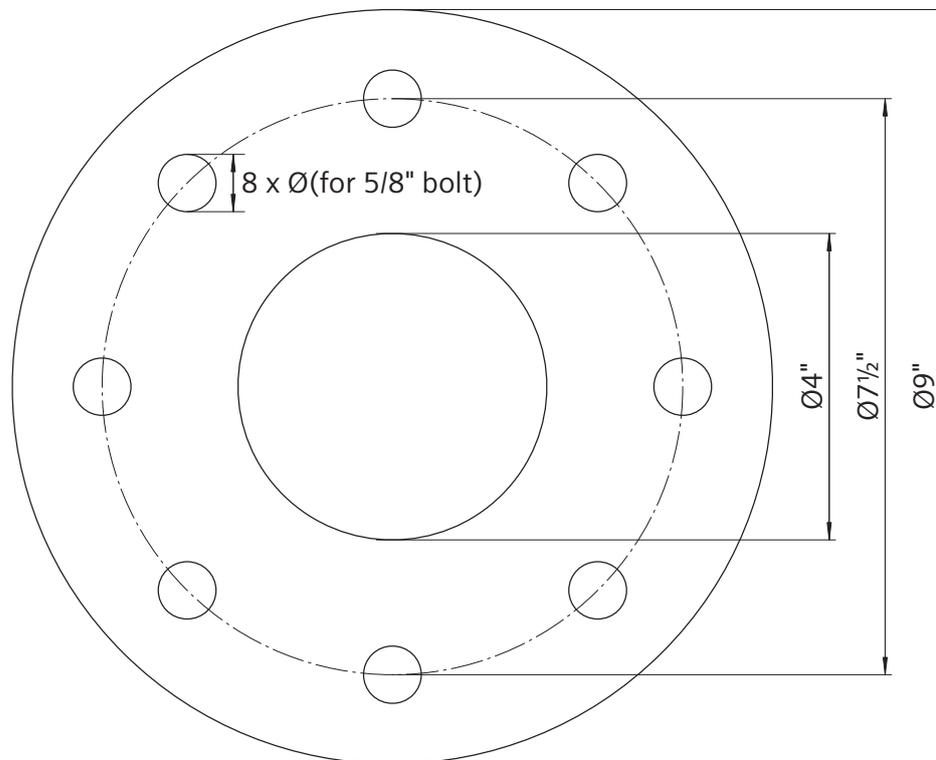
Dimensions de la bride ANSI 4"/150 lbs.
